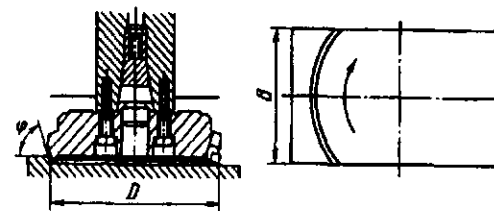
Схема фрезерования открытых плоских поверхностей торцовой фрезой
